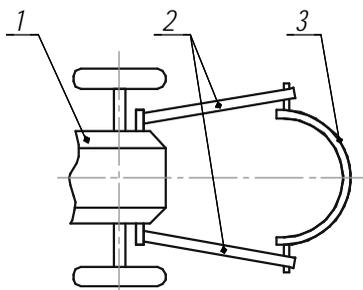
Схема агрегатирования косилки-плющилки с трактором:
